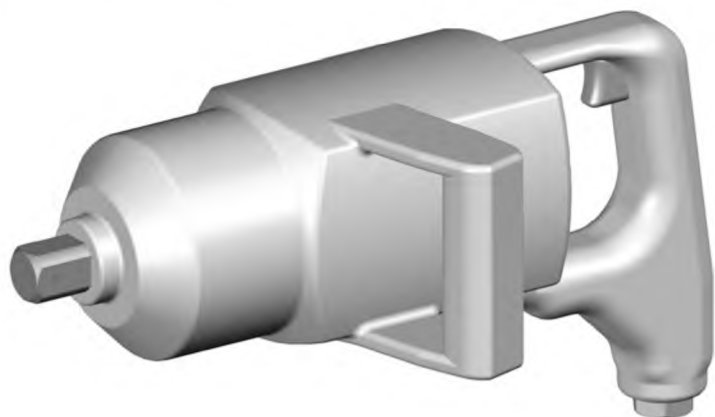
Ударный/импульсный гайковерт с дугообразными основной и поддерживающей рукоятками
